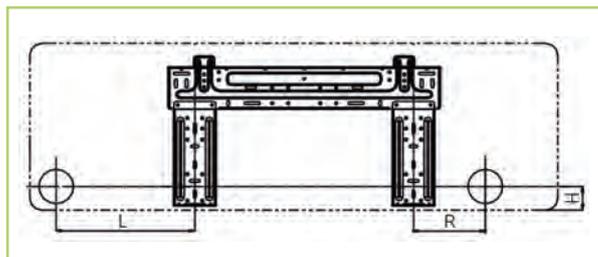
Montagepunkte der Wandhalterung MXW 521 (Frontansicht, alle Maße in mm)
